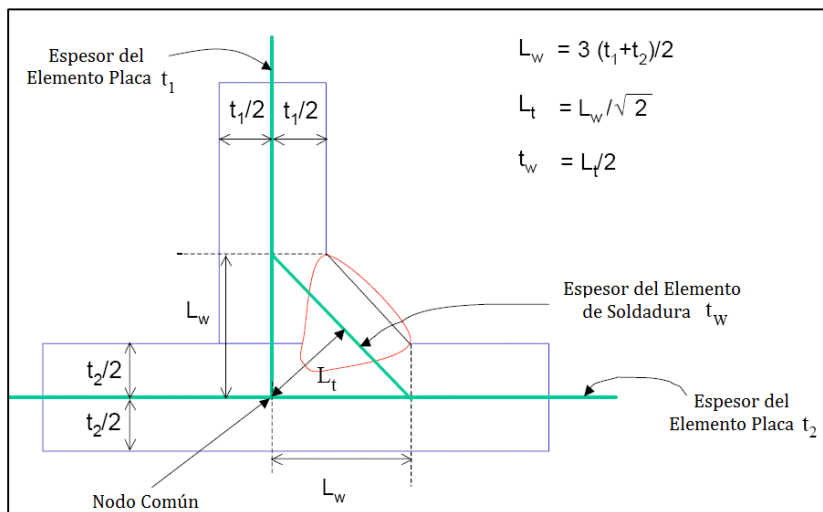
Modelado FEM Unión Soldada en "T" (Placas de Aluminio) [29]
